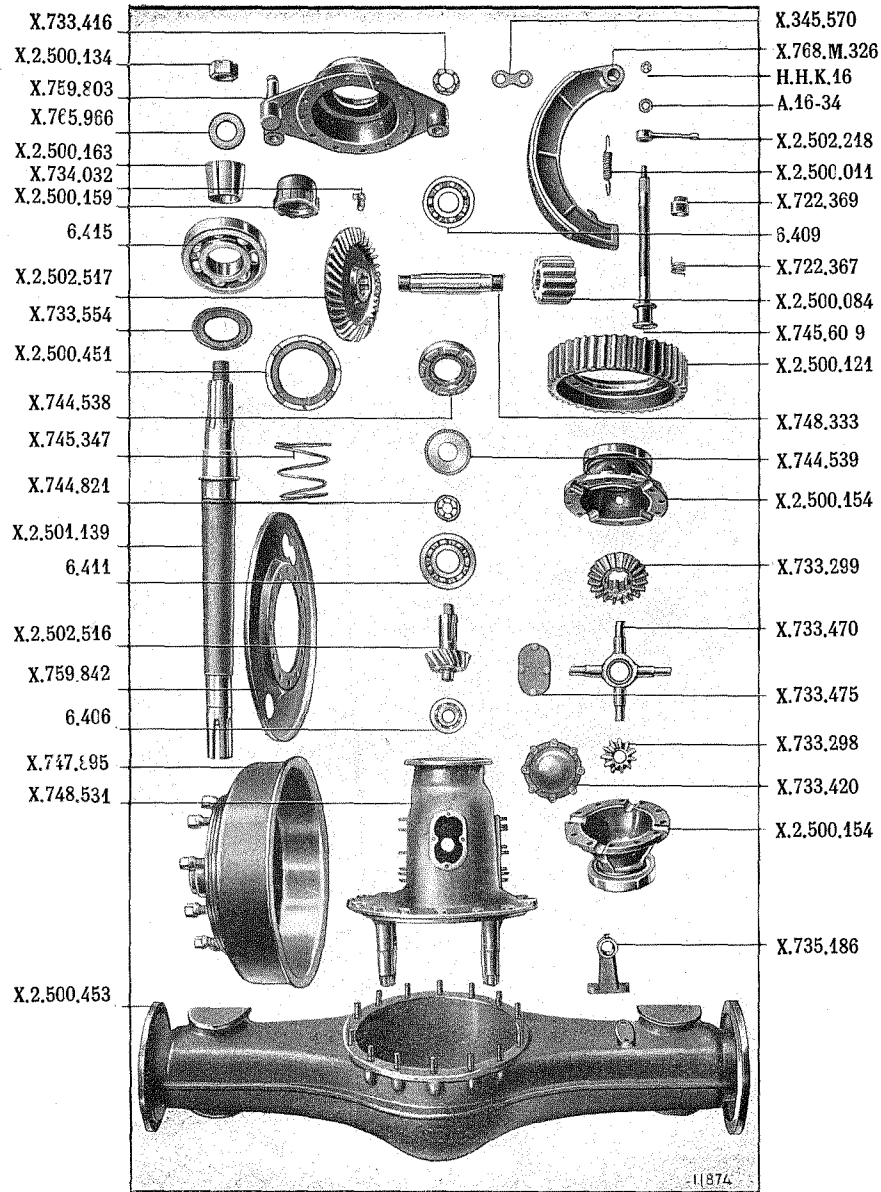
Pièces détachées de l'Essieu arrière, type T. L.
